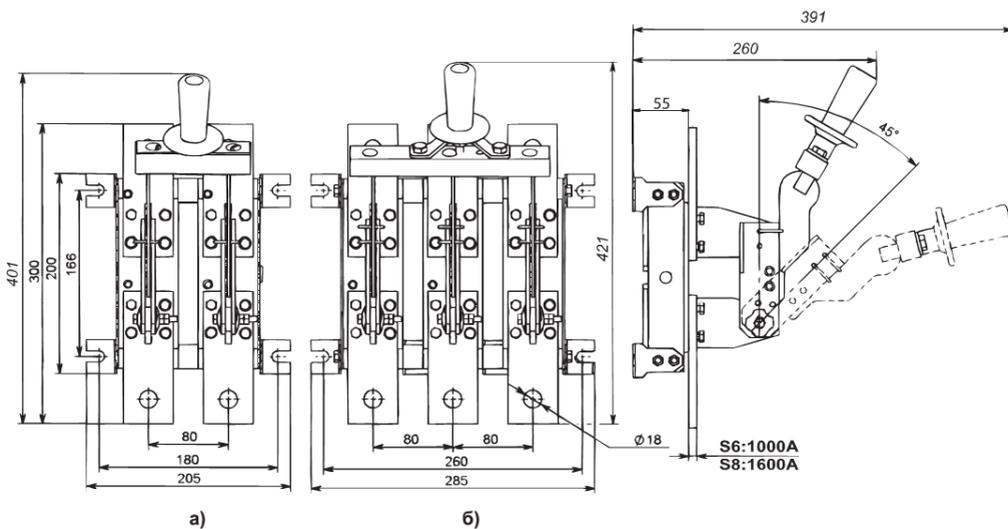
Разъединитель РЕ19 с центральным рычагом для управления штангой, заднего присоединения шин
